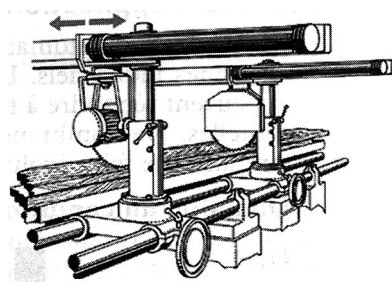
L'industrie du bois avec les opérations de débit, de sciage et d'usinage du bois
